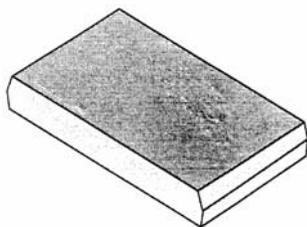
Покрытие заготовки штампа фоторезистом
